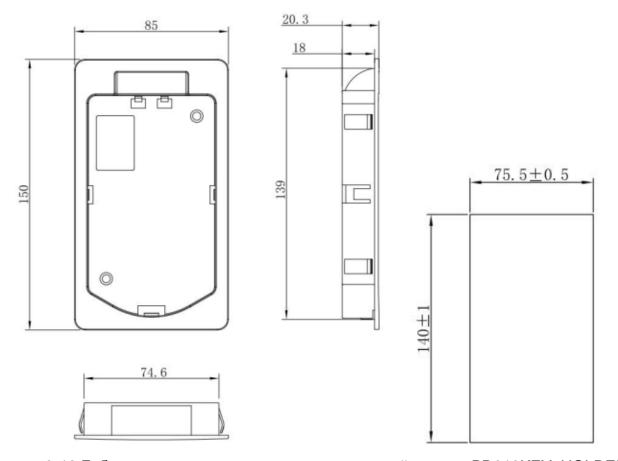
Габаритные размеры держателя кнопочной панели PD310KEY_HOLDER.
